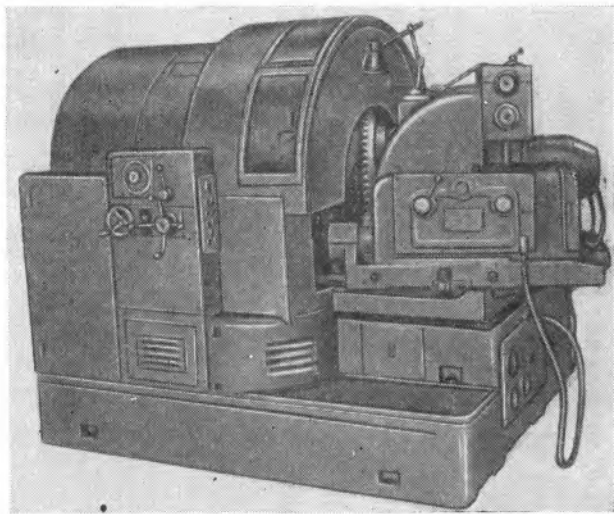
Зубошлифовальный полуавтомат 5B872 для обработки конических зубчатых колес
